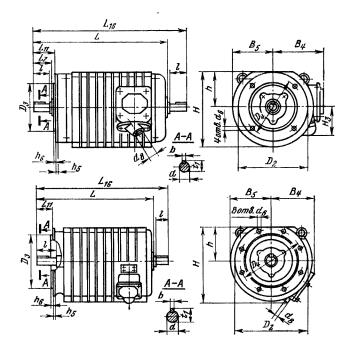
Габаритные и установочные размеры двигателей серии APФ 4—7-го габаритов.
